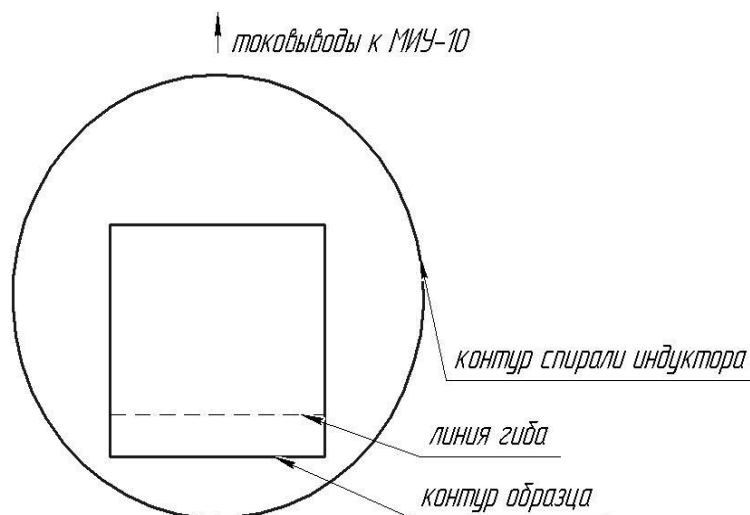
Схема установки квадратных образцов под круглым индуктором
